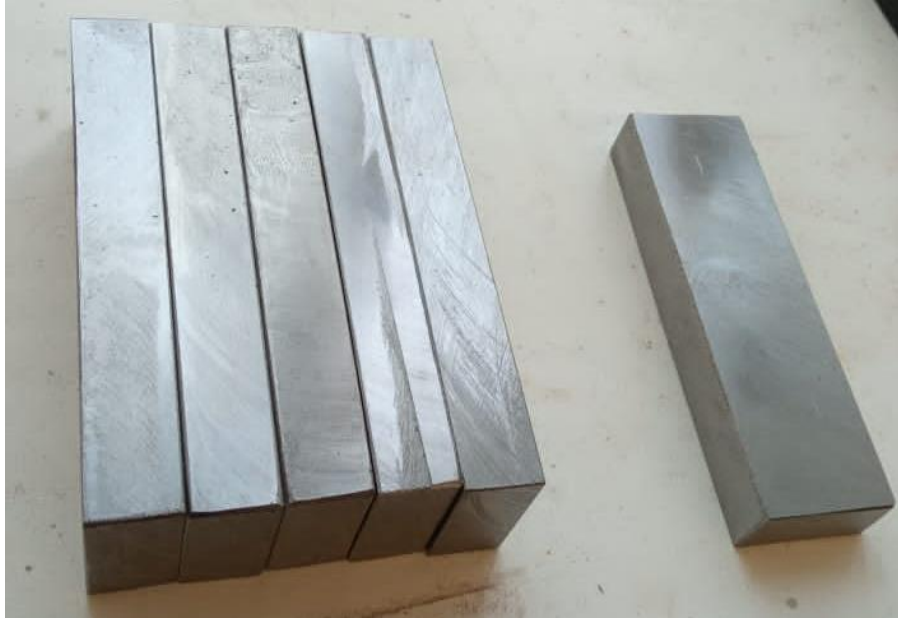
Образцы контрольных сварных соединений после вырезки
